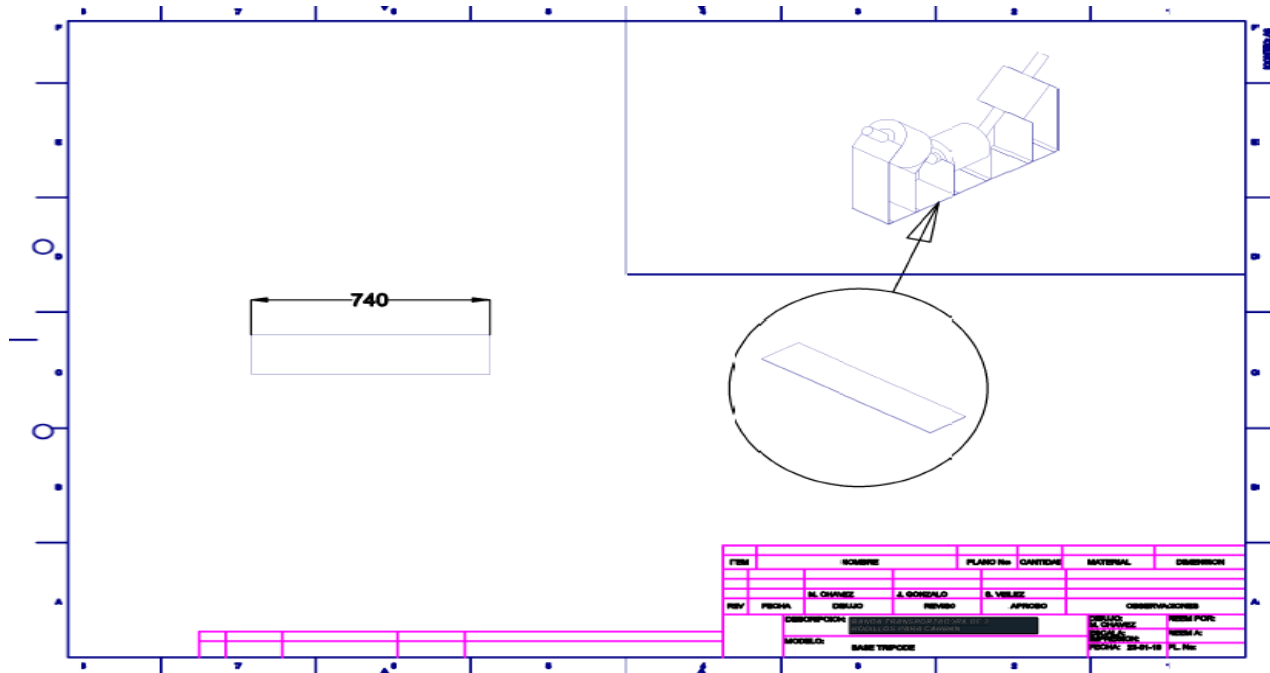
Plano detallado de la placa de soporte del sistema de rodillo.
